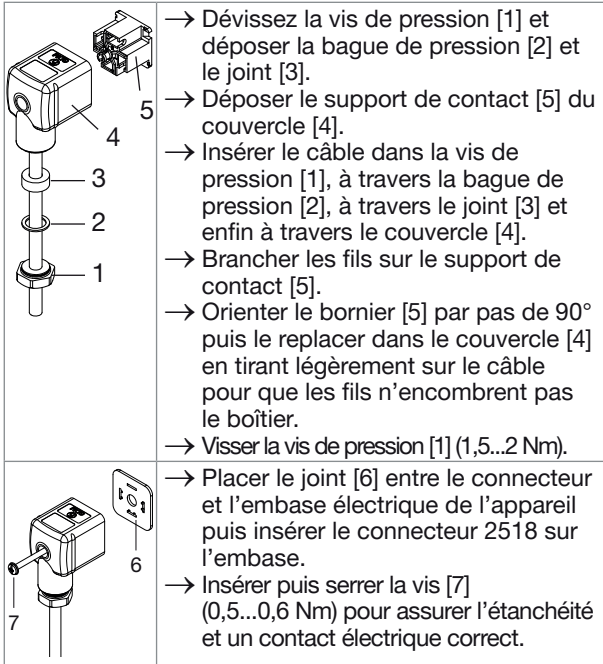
Assemblage du connecteur femelle type 2518 (fourni)
